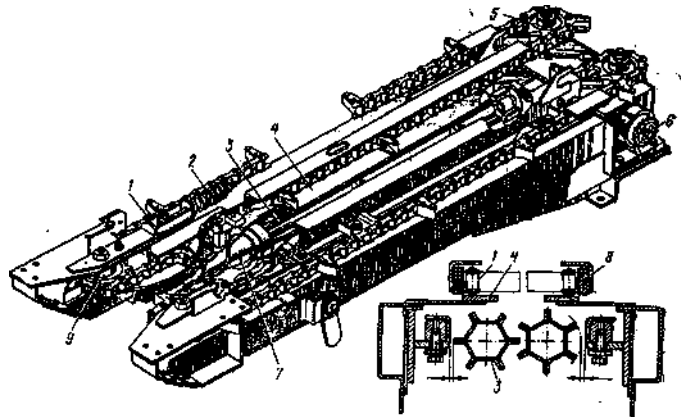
Схема пікerno-стреперного качановідокремлювального апарата: 1 - транспортуючий ланцюг; 2 - натяжний пристрій входної зірочки, 3 - протягуючі вальці; 4 - стріперні пластини; 5 - ведуча зірочка транспортуючого ланцюга; 6 - привідний вал апарату; 7 - західний конус протягуючого вальця, 8 - входна зірочка.
